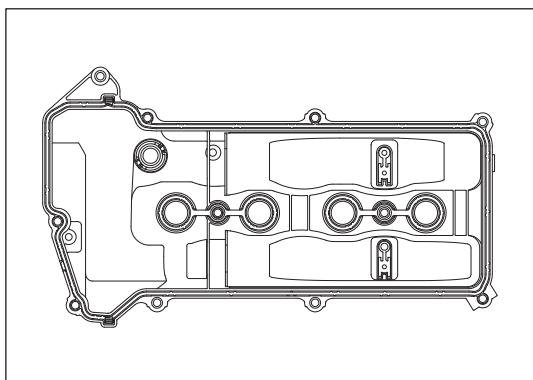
Проверка крышки головки блока цилиндров
